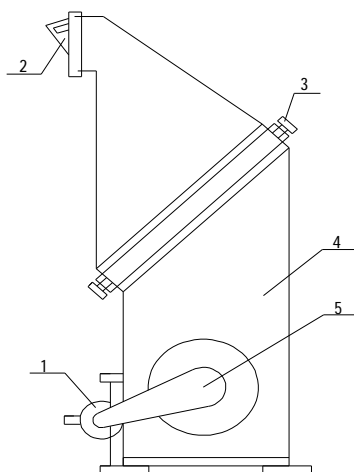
Напольный воздушно-рециркуляционный отопительный агрегат: 1 электродвигатель; 2 воздуховыпускной патрубок; 3 воздухонагреватель; 4 корпус; 5 клиноременная передача в защитном кожухе
